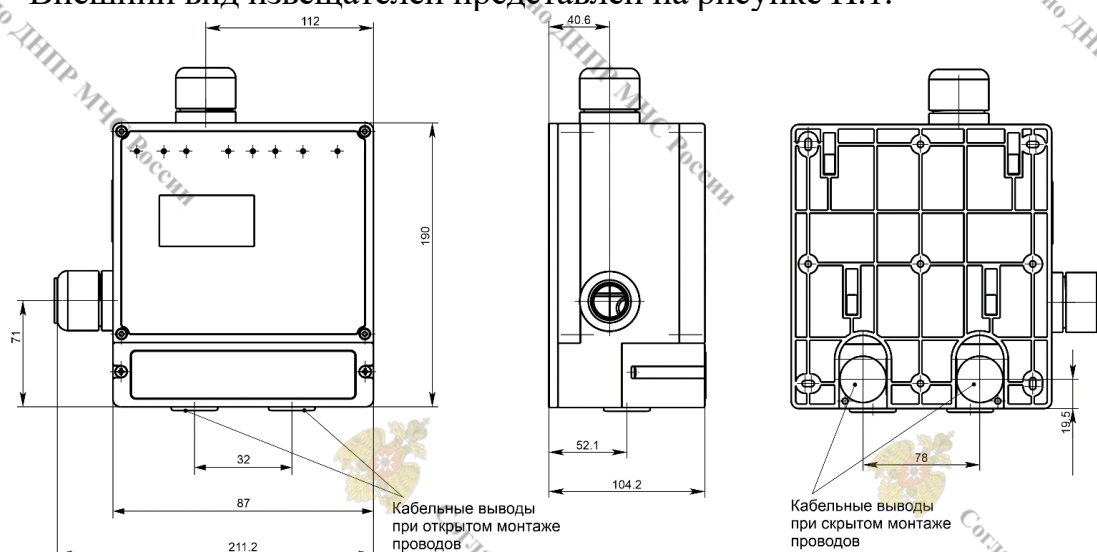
Внешний вид и габаритные размеры извещателей «ИП 212-4» и «ИП 212-5»
